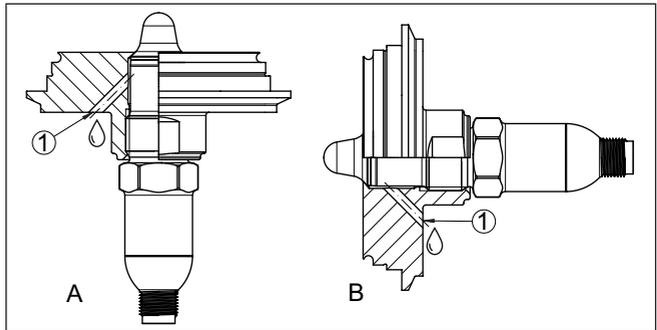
Ausrichtung des Einschweißstutzen
